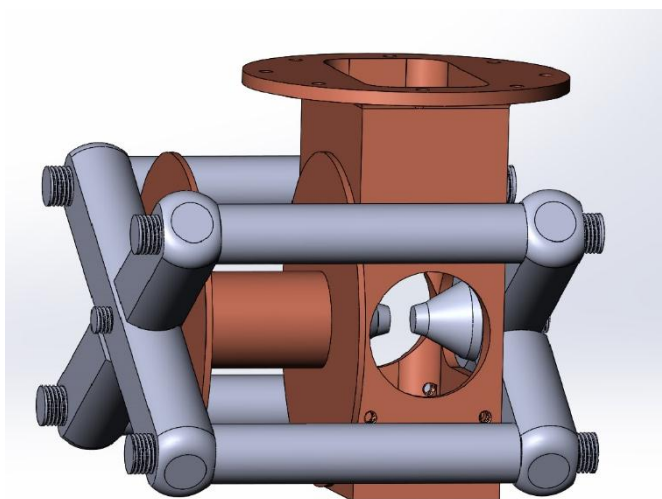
Аксонометрический сборочный чертеж магнитной ячейки.
